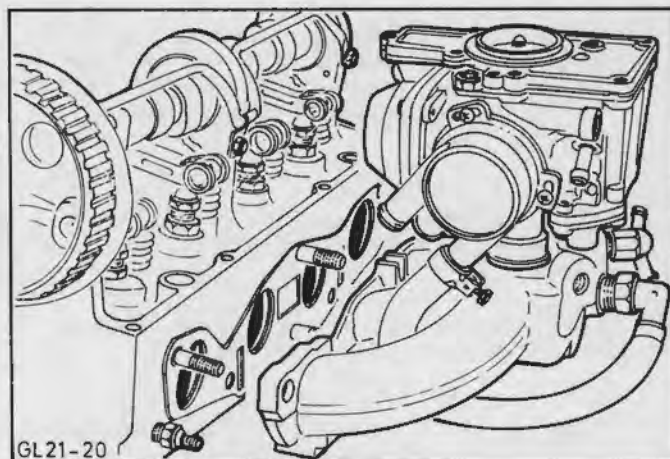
Afmonter indsugningsmanifold med karburator (1,6 ltr. motor vist)
